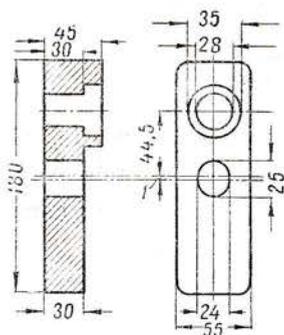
Деталь приспособления для проточки коленчатого вала J1-3/2
